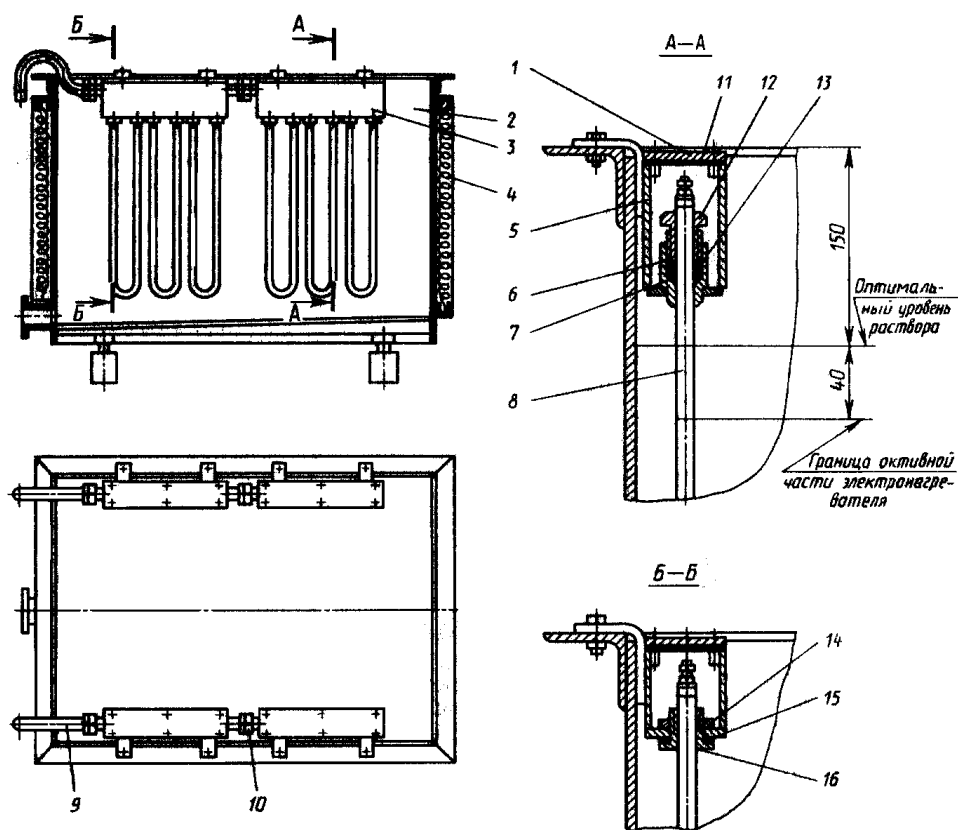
Ванна с электронагревателями: 1 — крышка; 2 — ванна; 3 — блок электронагревателей; 4 — теплоизоляция; 5 — корпус; 6 — стальная шайба; 7 — свинцовая шайба; 8 — электронагреватель; 9, 10 — трубопроводная арматура; 11 — уплотнительная прокладка; 12 — нажимная гайка; 13 — резьбовая втулка; 14 — гайка; 15 — уплотнительная прокладка; 16 — резьбовая втулка.
